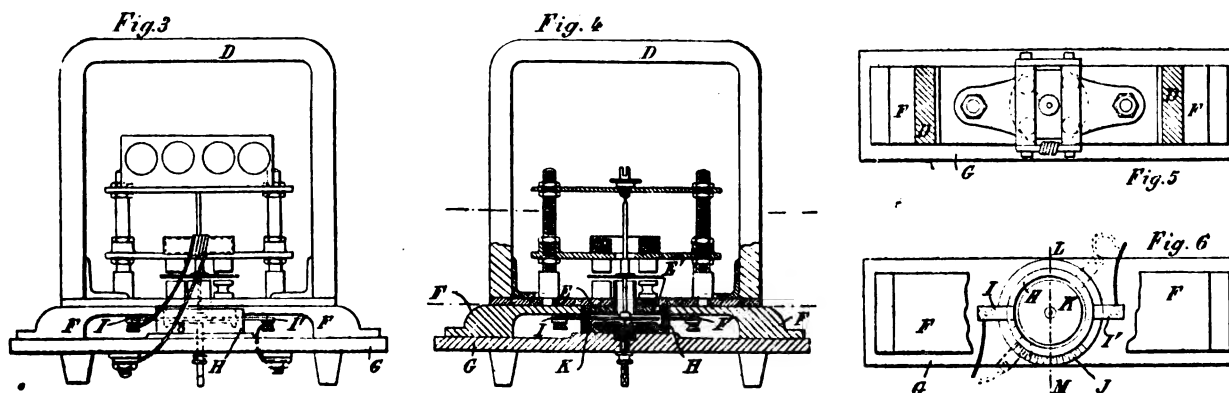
, 4, 5 et 6. — Elévation et coupe verticale, plan et coupe horizontale du compteur à mercure Hookham.
